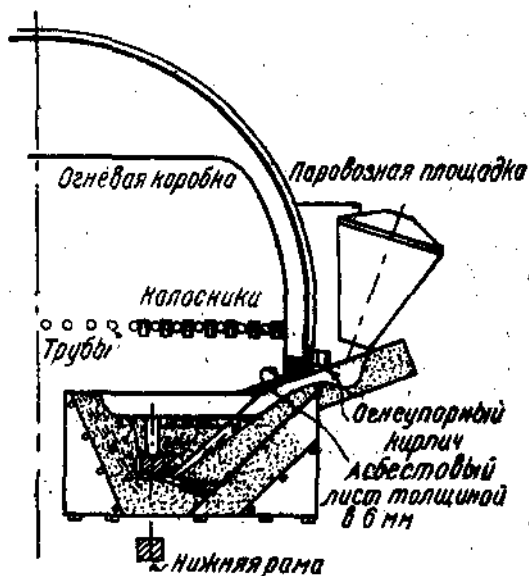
Способ, применяемый при производстве сварки в местах мало доступных. Жолоб в случае, если футеровка сделана из специального формовочного материала, должен быть перед употреблением в дело тщательно высушен. Для футеровки жолоба лучше всего применять смесь магнезии со смолой.
